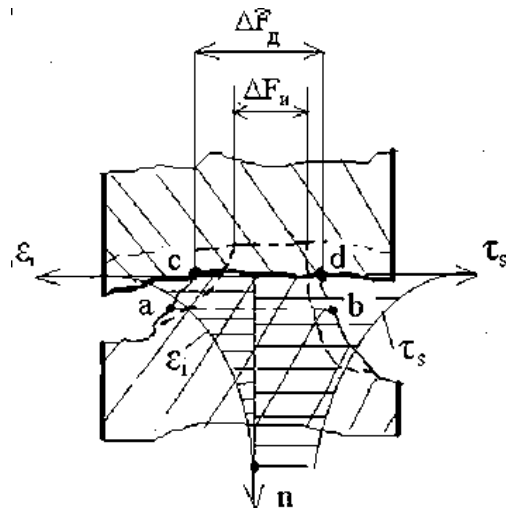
Процесс относительного перемещения заготовки по поверхности инструмента на площадке ΔF_i
